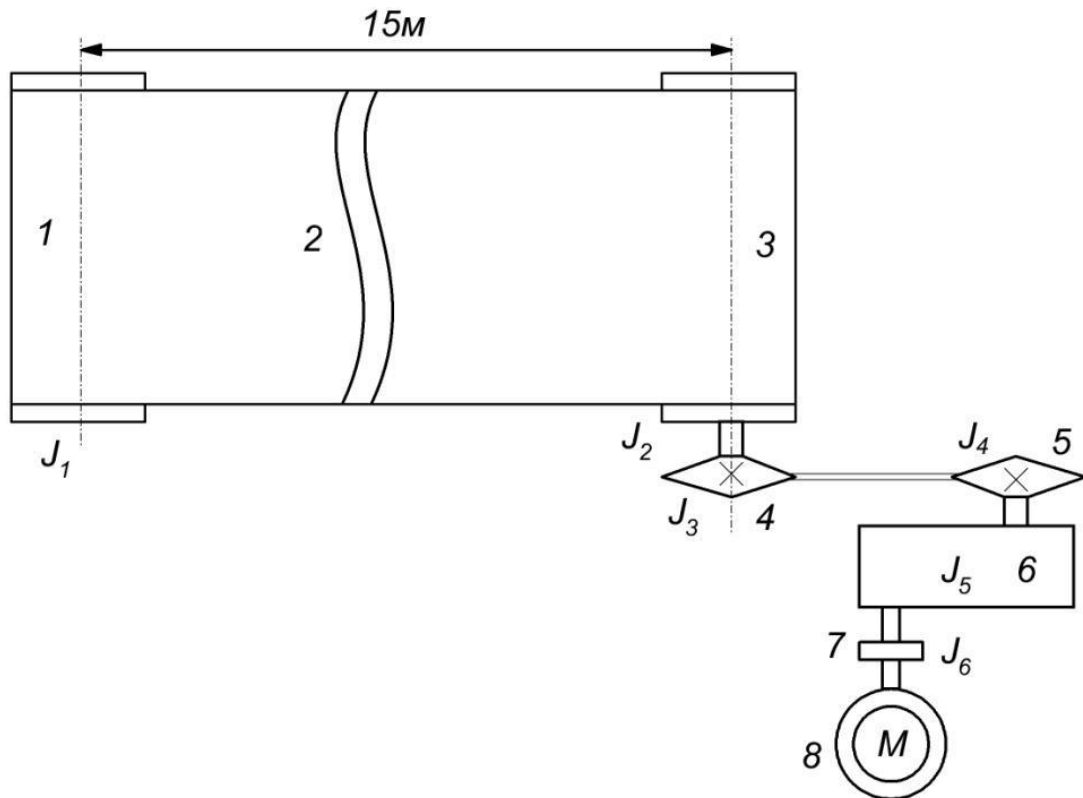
Кінематична схема приводу сітчастого пода (1-натяг Барабан; 2 сітчаста піч; 3 приводний барабан; 4,5 ланцюгова передача; 6 – Циліндричний редуктор; 7 - сполучна муфта; 8-електродвигун).
